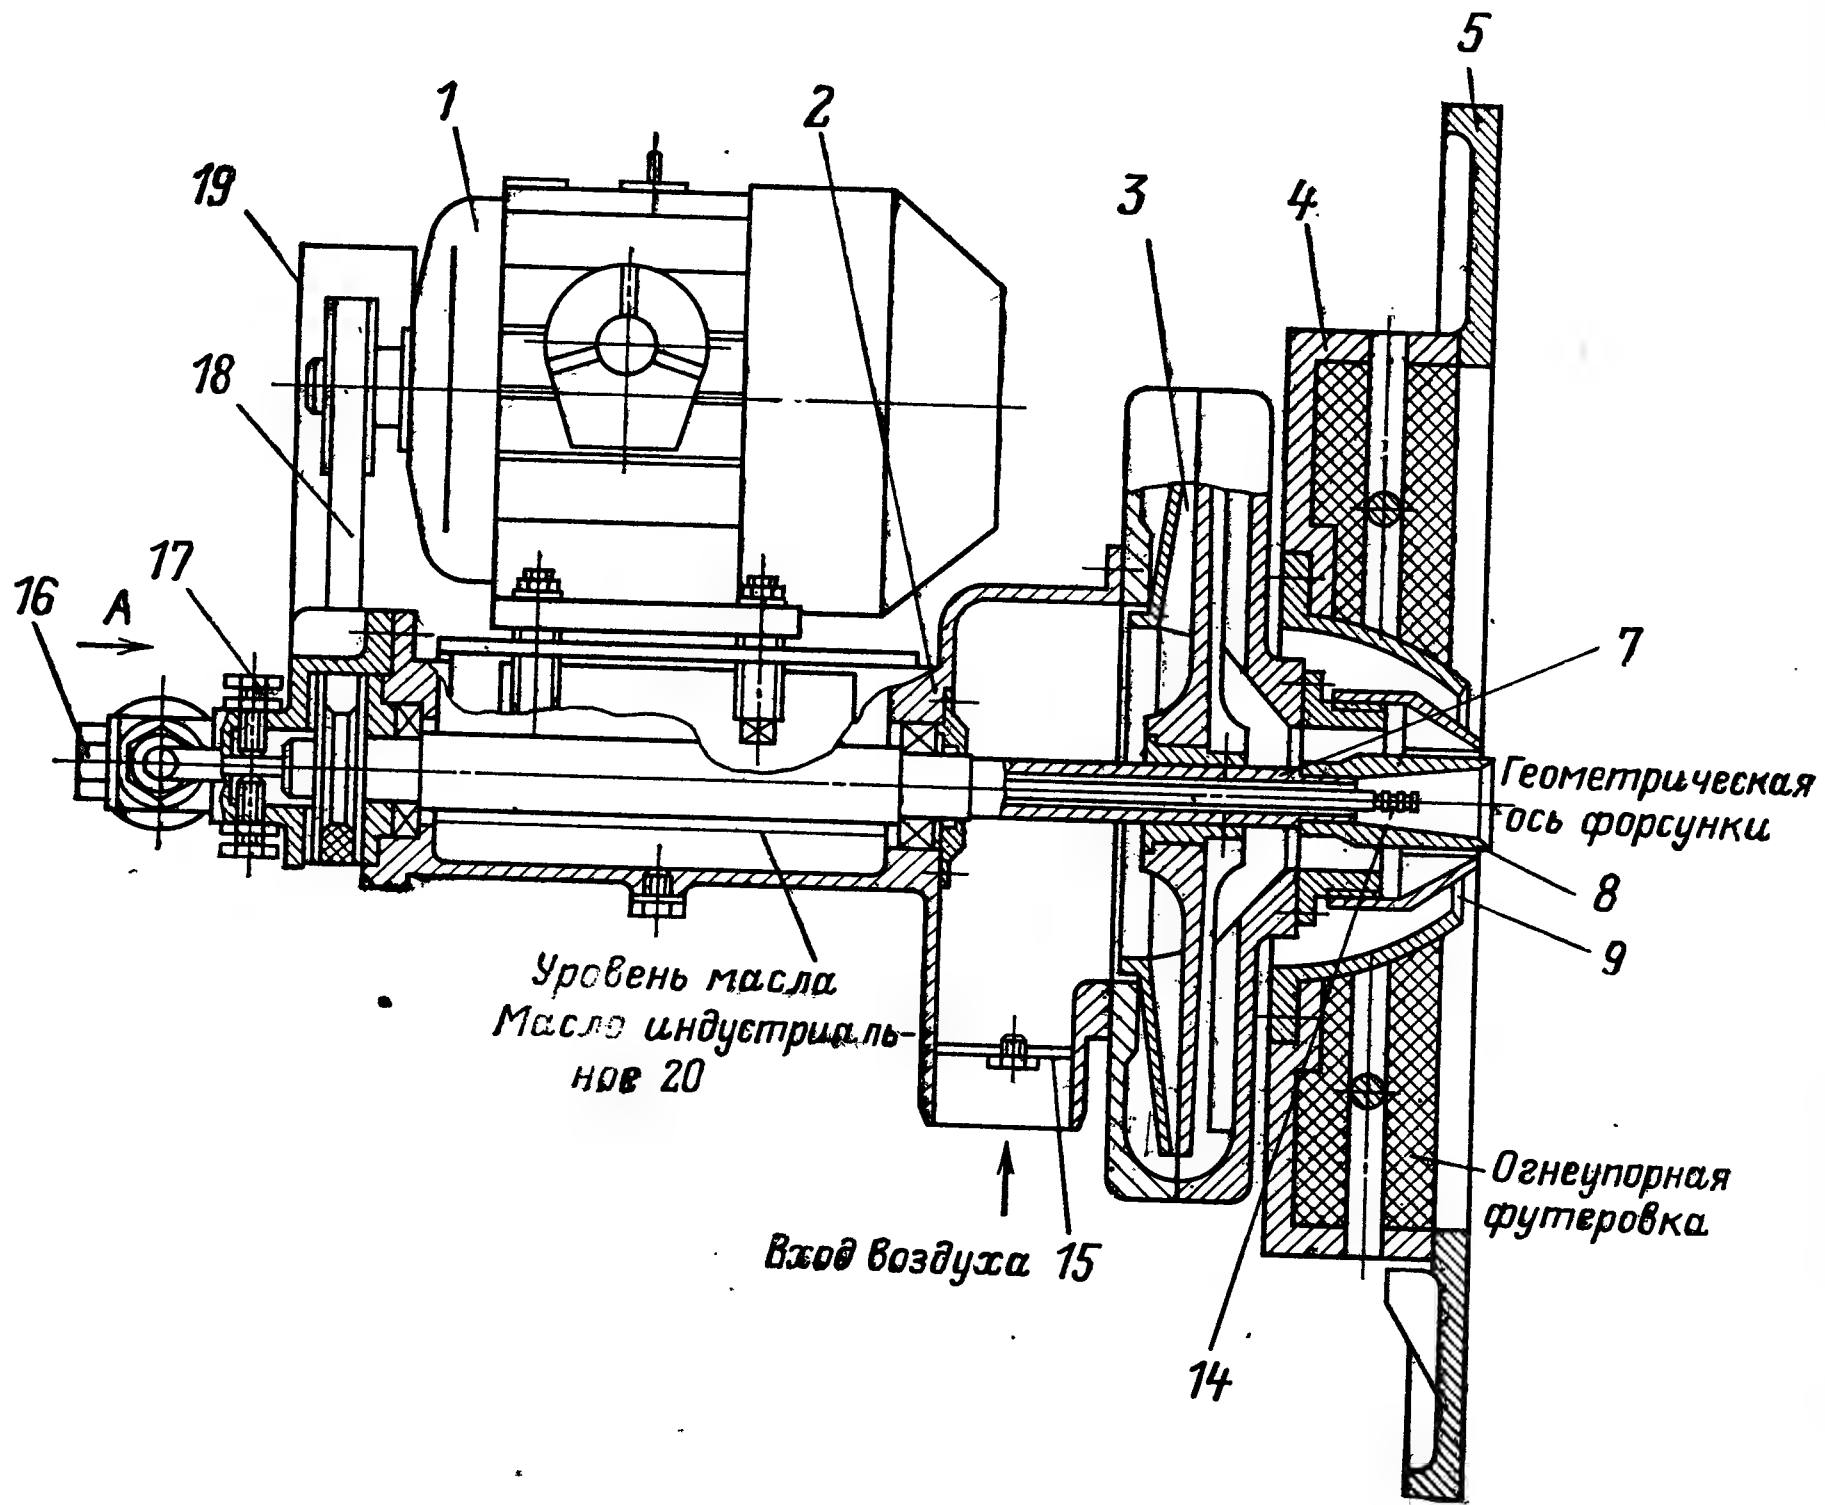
Форсунка, распыливающая жидкое топливо; 1 — электродвигатель; 2 — корпус форсунки; 3 — вентилятор; 4 — дверца топki; 5 — плита; 6 — ось вывертывания форсунки; 10 — ось вывертывания форсунки; 11 — скоба крепления дверцы топki; 12 — ручка заслонки, регулирования расхода воздуха на распыливание; 16 — пробка для очистки вентиля; 17 —
